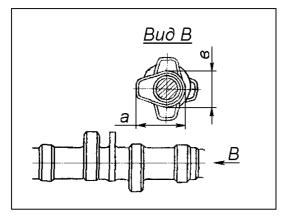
К контролю высоты кулачка кулачкового вала: а – размер от затылка до вершины кулачка; в – диаметр цилиндрической части кулачка.
